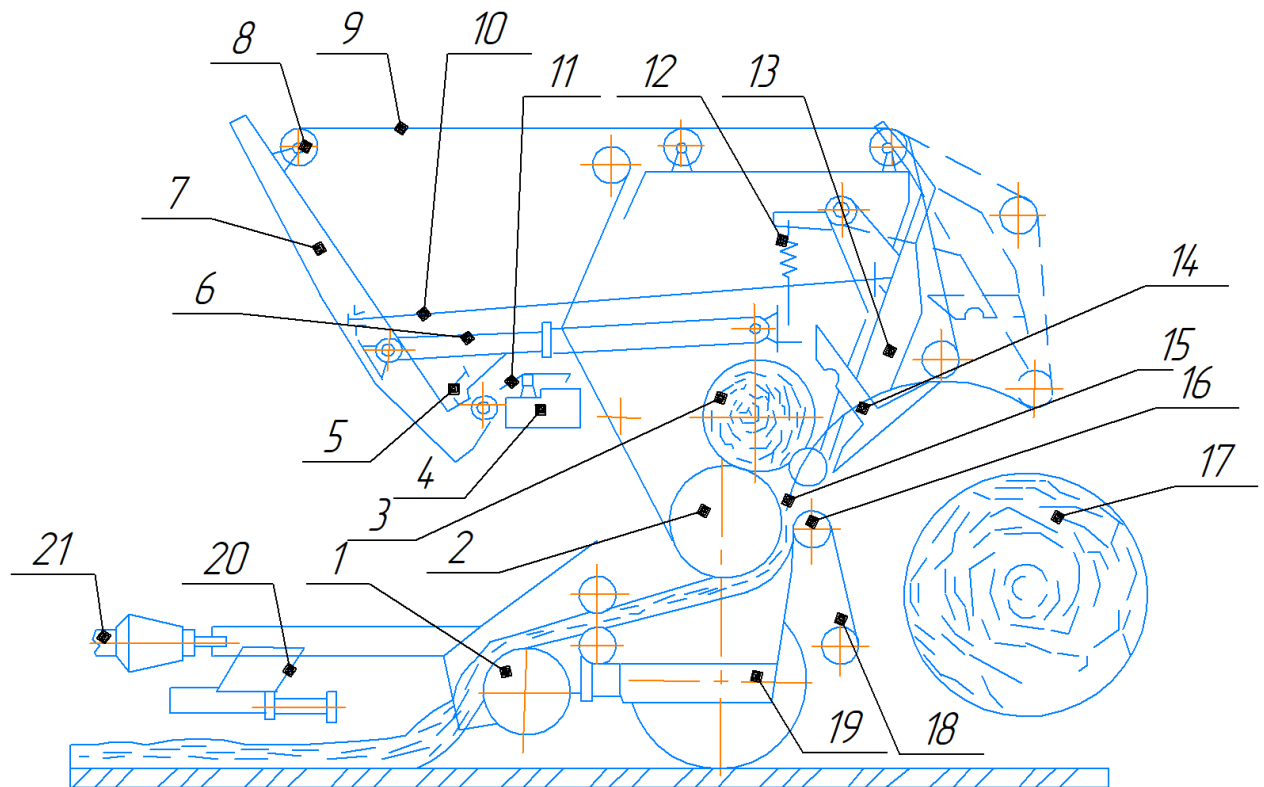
Конструктивна схема прес-підбирача ПРП-1,6: 1 – підбираючий пристрій; 2 – барабан; 3 – камера пресування; 4 – механізм вмикання та приводу обмотуючого апарата; 5 – сектор вмикання; 6 – гідроциліндр; 7 – натяжна рамка; 8 – валик; 9 – пресуючий пас; 10 – штанга; 11 – важіль вмикання; 12 – пружина; 13 – клапан; 14 – защіпка; 15 – відсікач; 16 – рухомий валик; 17 – рулон; 18 – транспортер; 19 – ходова частина; 20 – причіпний пристрій; 21 – карданна передача.
